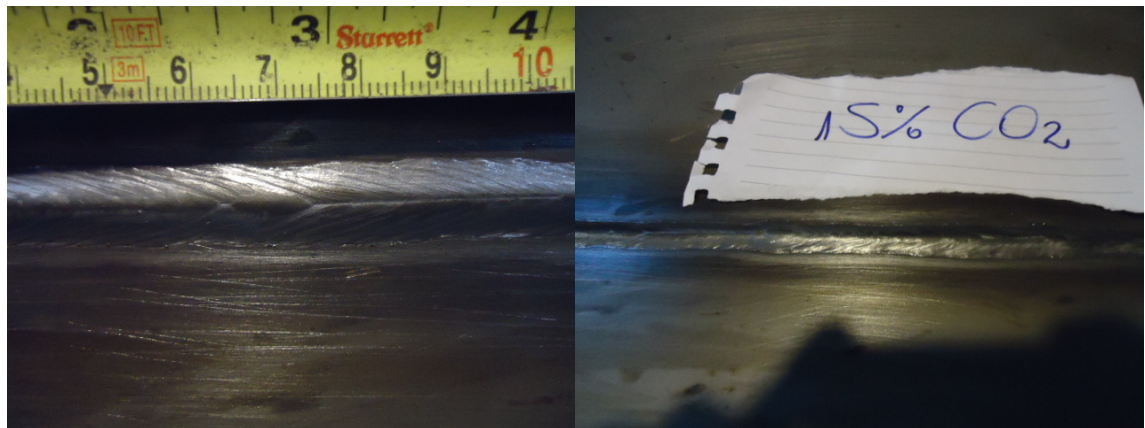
Chapa teste soldada com mistura 15% CO_2
